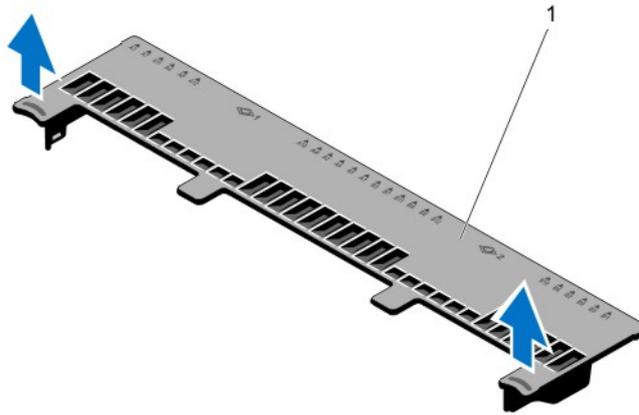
Entfernen und Einsetzen des Kühlgehäuses
